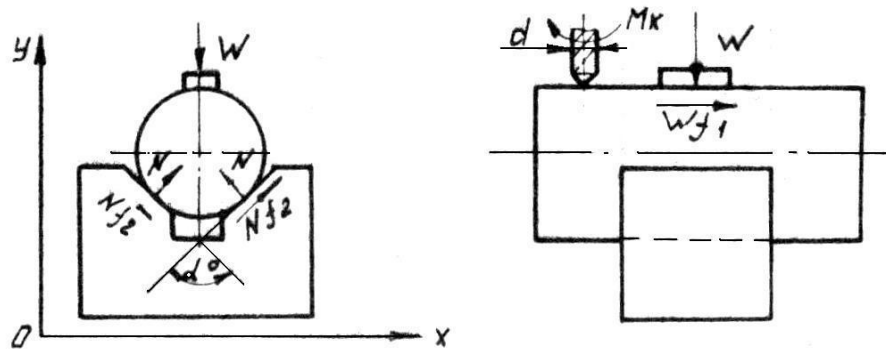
Схема розрахунку затискних зусиль при обробці заготовки на свердлильному верстаті установленій в призмі з прихватом
